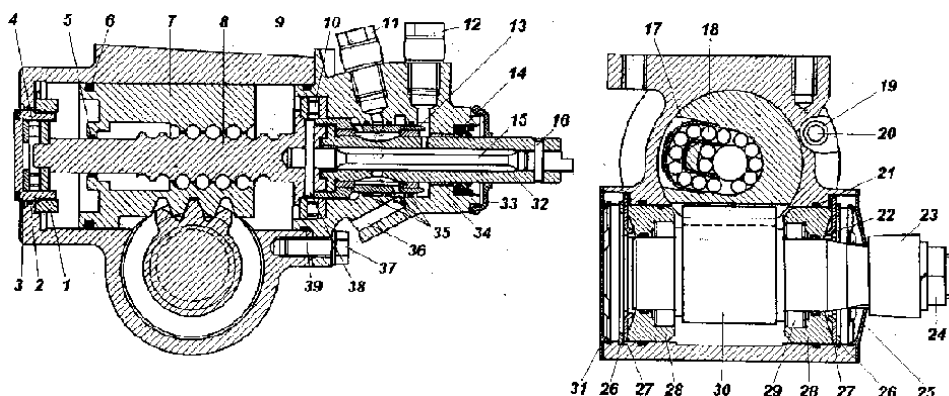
Рулевой механизм с гидроусилителем: 1 -гайка; 2, 19, 21, 22, 35, 39 -уплотнительные кольца; 3 -стакан; 4, 10 -упорные подшипники; 5, 6 -уплотнители; 7 -поршень-рейка; 8 -винт; 9 -картер; 11 -штуцер нагнетательного шланга; 12 -штуцер сливного шланга; 13 -гильза; 14 -манжета; 15 -торсион; 16, 38 -штифты; 17 -шариковод; 18 -шарики; 20 -канал в картере; 23 -сошка; 24 -гайка сошки; 25 -Крышка защитная нижняя; 26 -стопорные кольца; 27 -регулирующие шайбы; 28 -опоры вала сошки; 29 -ролики; 30 -вал сошки; 31 -крышка защитная верхняя; 32 -ротор; 33 -защитный колпак; 34 -корпус распределителя; 36 -канал в корпусе распределителя; 37 -болты крепления корпуса распределителя к картеру.
